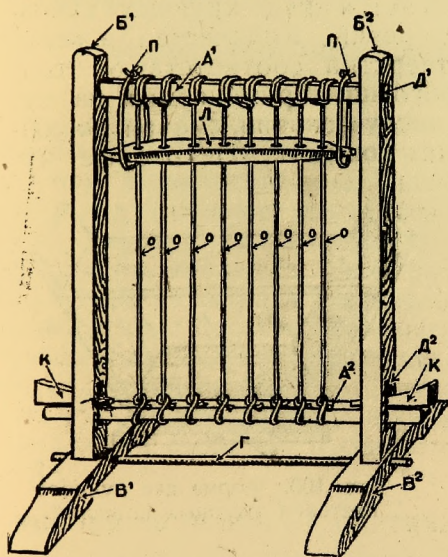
Одинарный станок (верстак) с натянутой основой.
